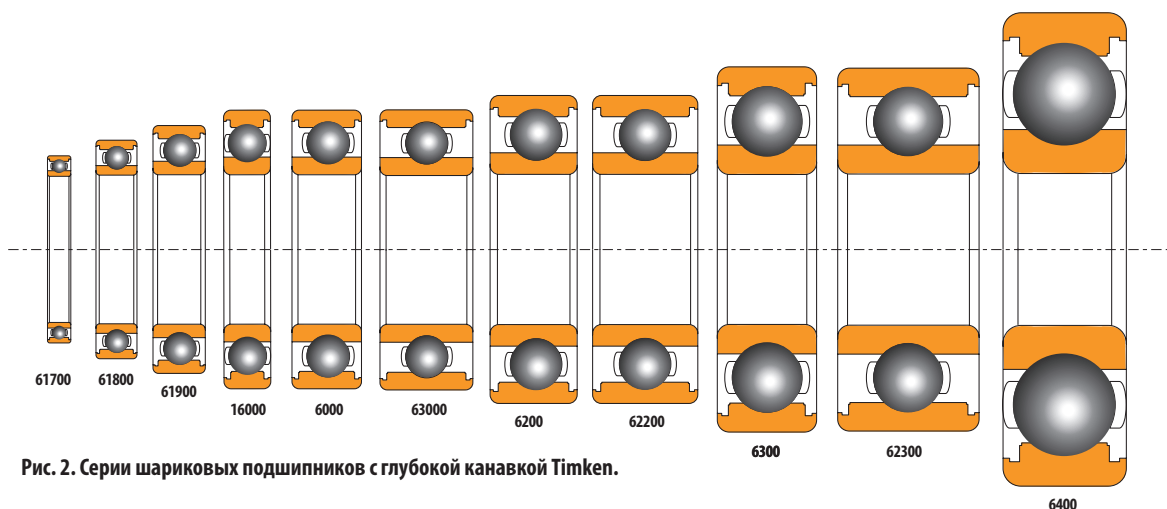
Серии шариковых подшипников с глубокой канавкой Timken.
